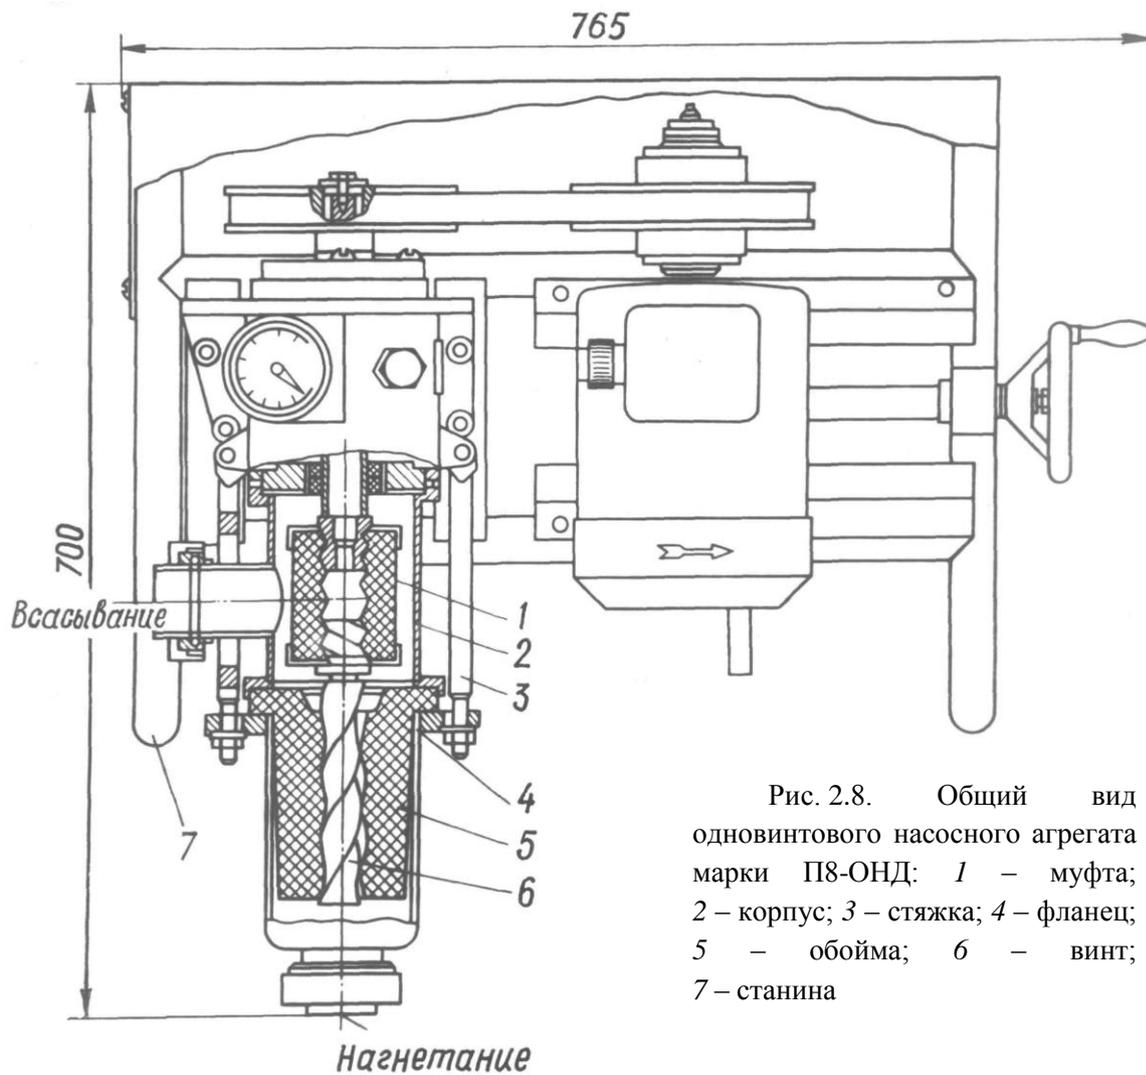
Общий вид одновинтового насосного агрегата марки П8-ОНД: 1 – муфта; 2 – корпус; 3 – стяжка; 4 – фланец; 5 – обойма; 6 – винт; 7 – станина
